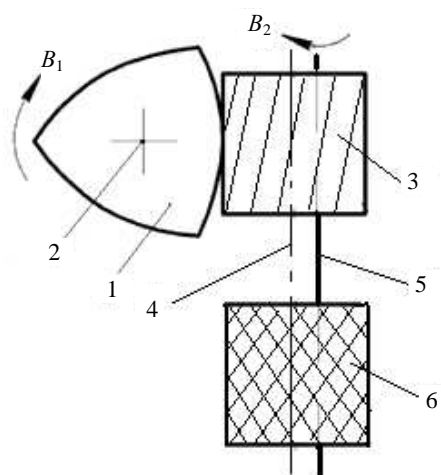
Схема инструментальной наладки для последовательной обработки некруглой поверхности двумя инструментами
